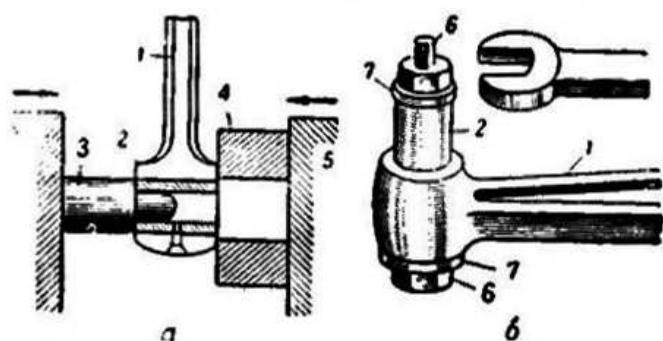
Способы выпрессовки и запрессовки втулки верхней головки шатуна:
